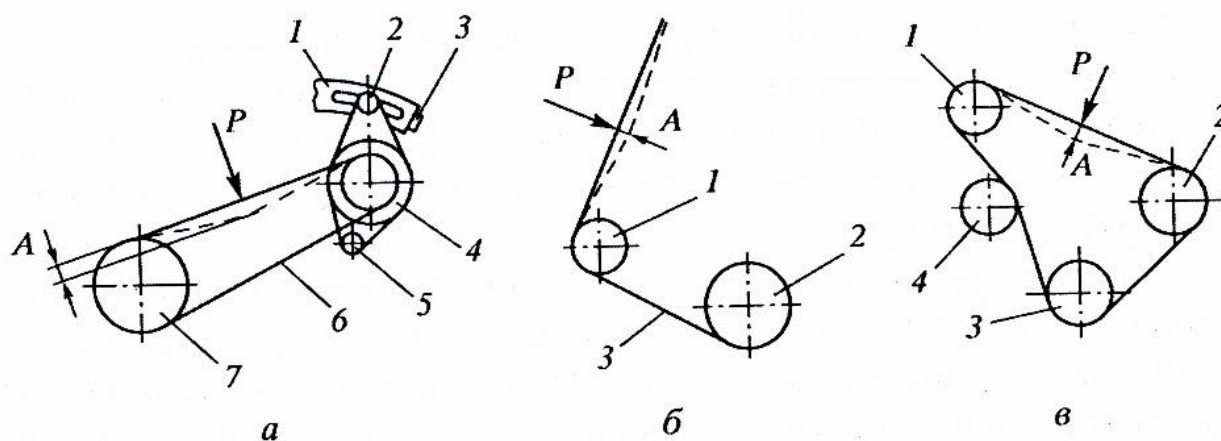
Схемы приводных механизмов генераторных установок: а – привод автомобилей типа ВАЗ-2110: 1 – верхний кронштейн генератора; 2 – гайка; 3 – регулировочный болт; 4 – генератор; 5 – болт шарнирного крепления; 6 – ремень; 7 – ведущий шкив на коленчатом валу; б – привод автомобилей с двигателем ЗМЗ-4025, 4026: 1 – шкив генератора; 2 – ведущий шкив на коленчатом валу; 3 – ремень; в – привод автомобилей с двигателем ГАЗ-560 (дизель): 1 – генератор; 2 – привод вентилятора; 3 – ведущий шкив на коленчатом валу; 4 – автоматический механизм натяжения ремня с помощью спиральной пружины
